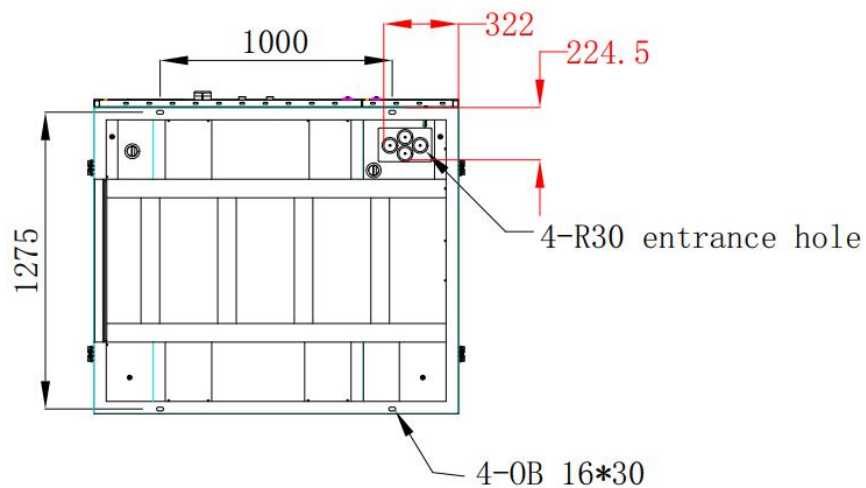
Estructura inferior del gabinete de la batería (vista inferior)
